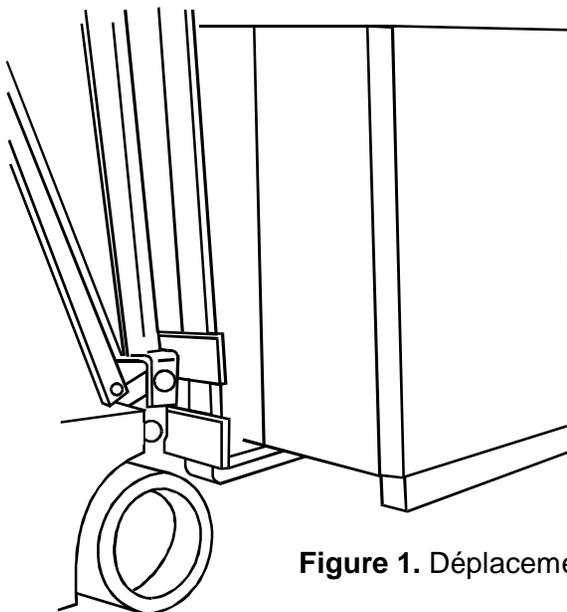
Déplacement de la machine à laminer à l'aide d'un chariot élévateur
